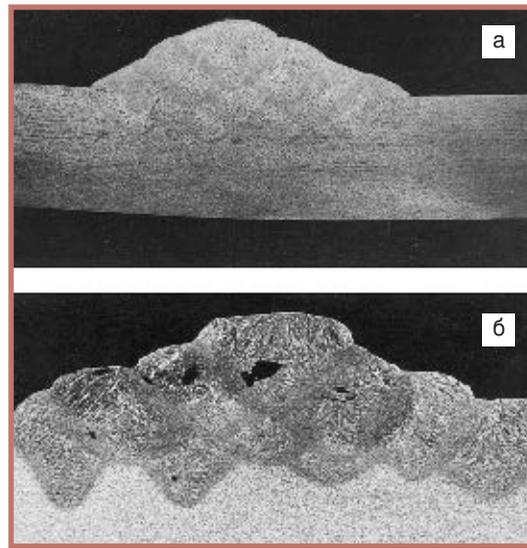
Влияние конструкции горелки на образование пористости металла шва при многопроходной сварке в смеси $Ar+18\% CO_2$: а — конусное сопло с цилиндрическим наконечником; б — цилиндрическое сопло с наконечником «сапожкового» типа ($I_{св} = 280$ А, $U_d = 28$ В, расход газа 20 л/мин, расстояние от сопла до пластины 20 мм, диаметр проволоки 1,2 мм); $\times 2$
